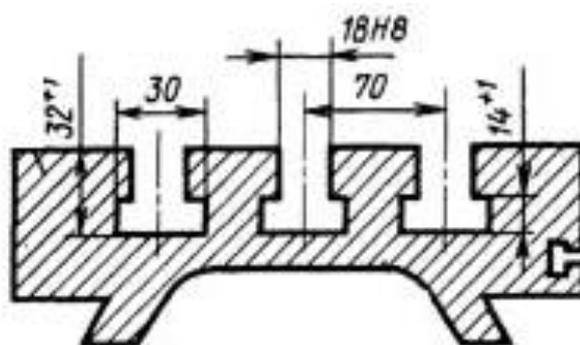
Рабочая область стола станка 6P12Б
